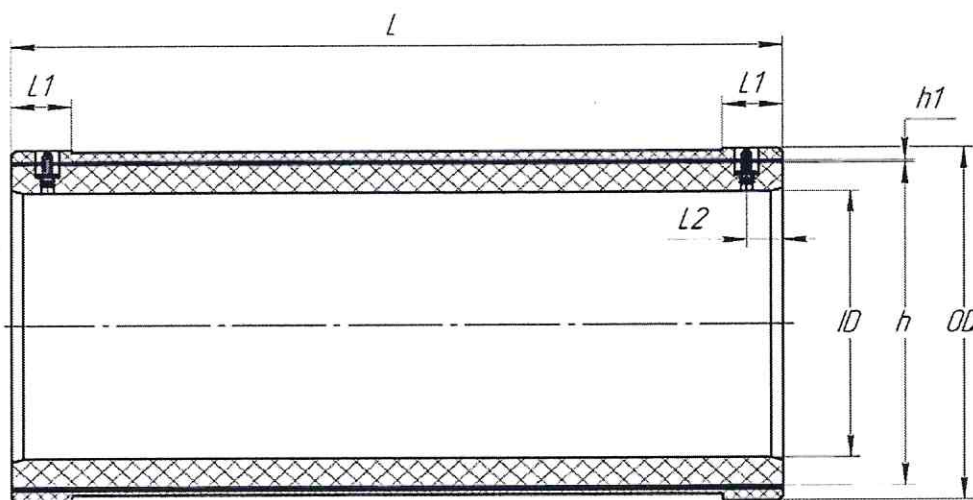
Общий вид фитинга с закладными нагревателями
